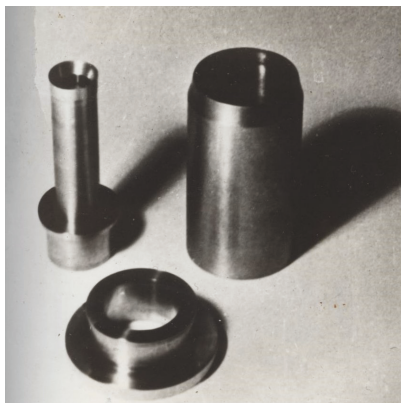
Приспособления для вырезки цилиндрических и трубчатых образцов грунтов
